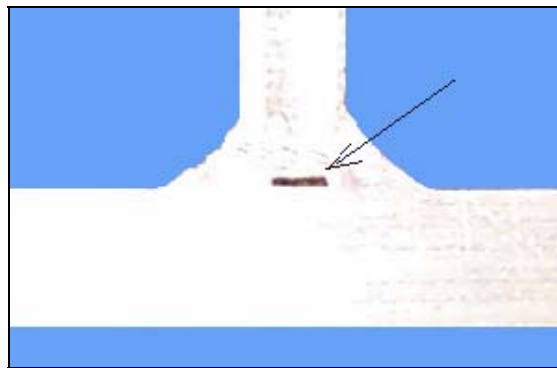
Défaut de 2 mm pour l'essai TGAP
